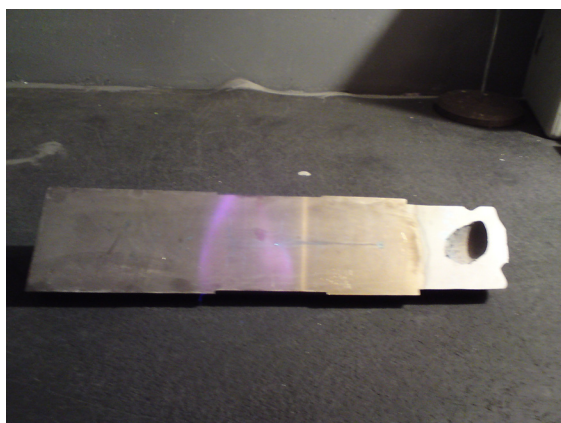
Темплет слитка, полученный литьем в металлический кокиль
